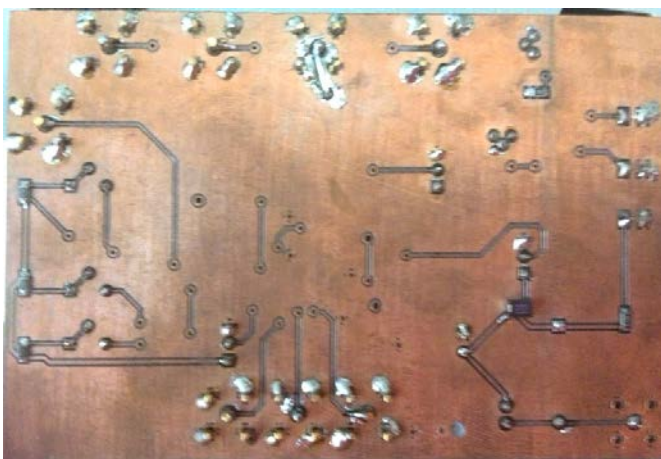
PCB con componentes soldados, capa BOTTOM
